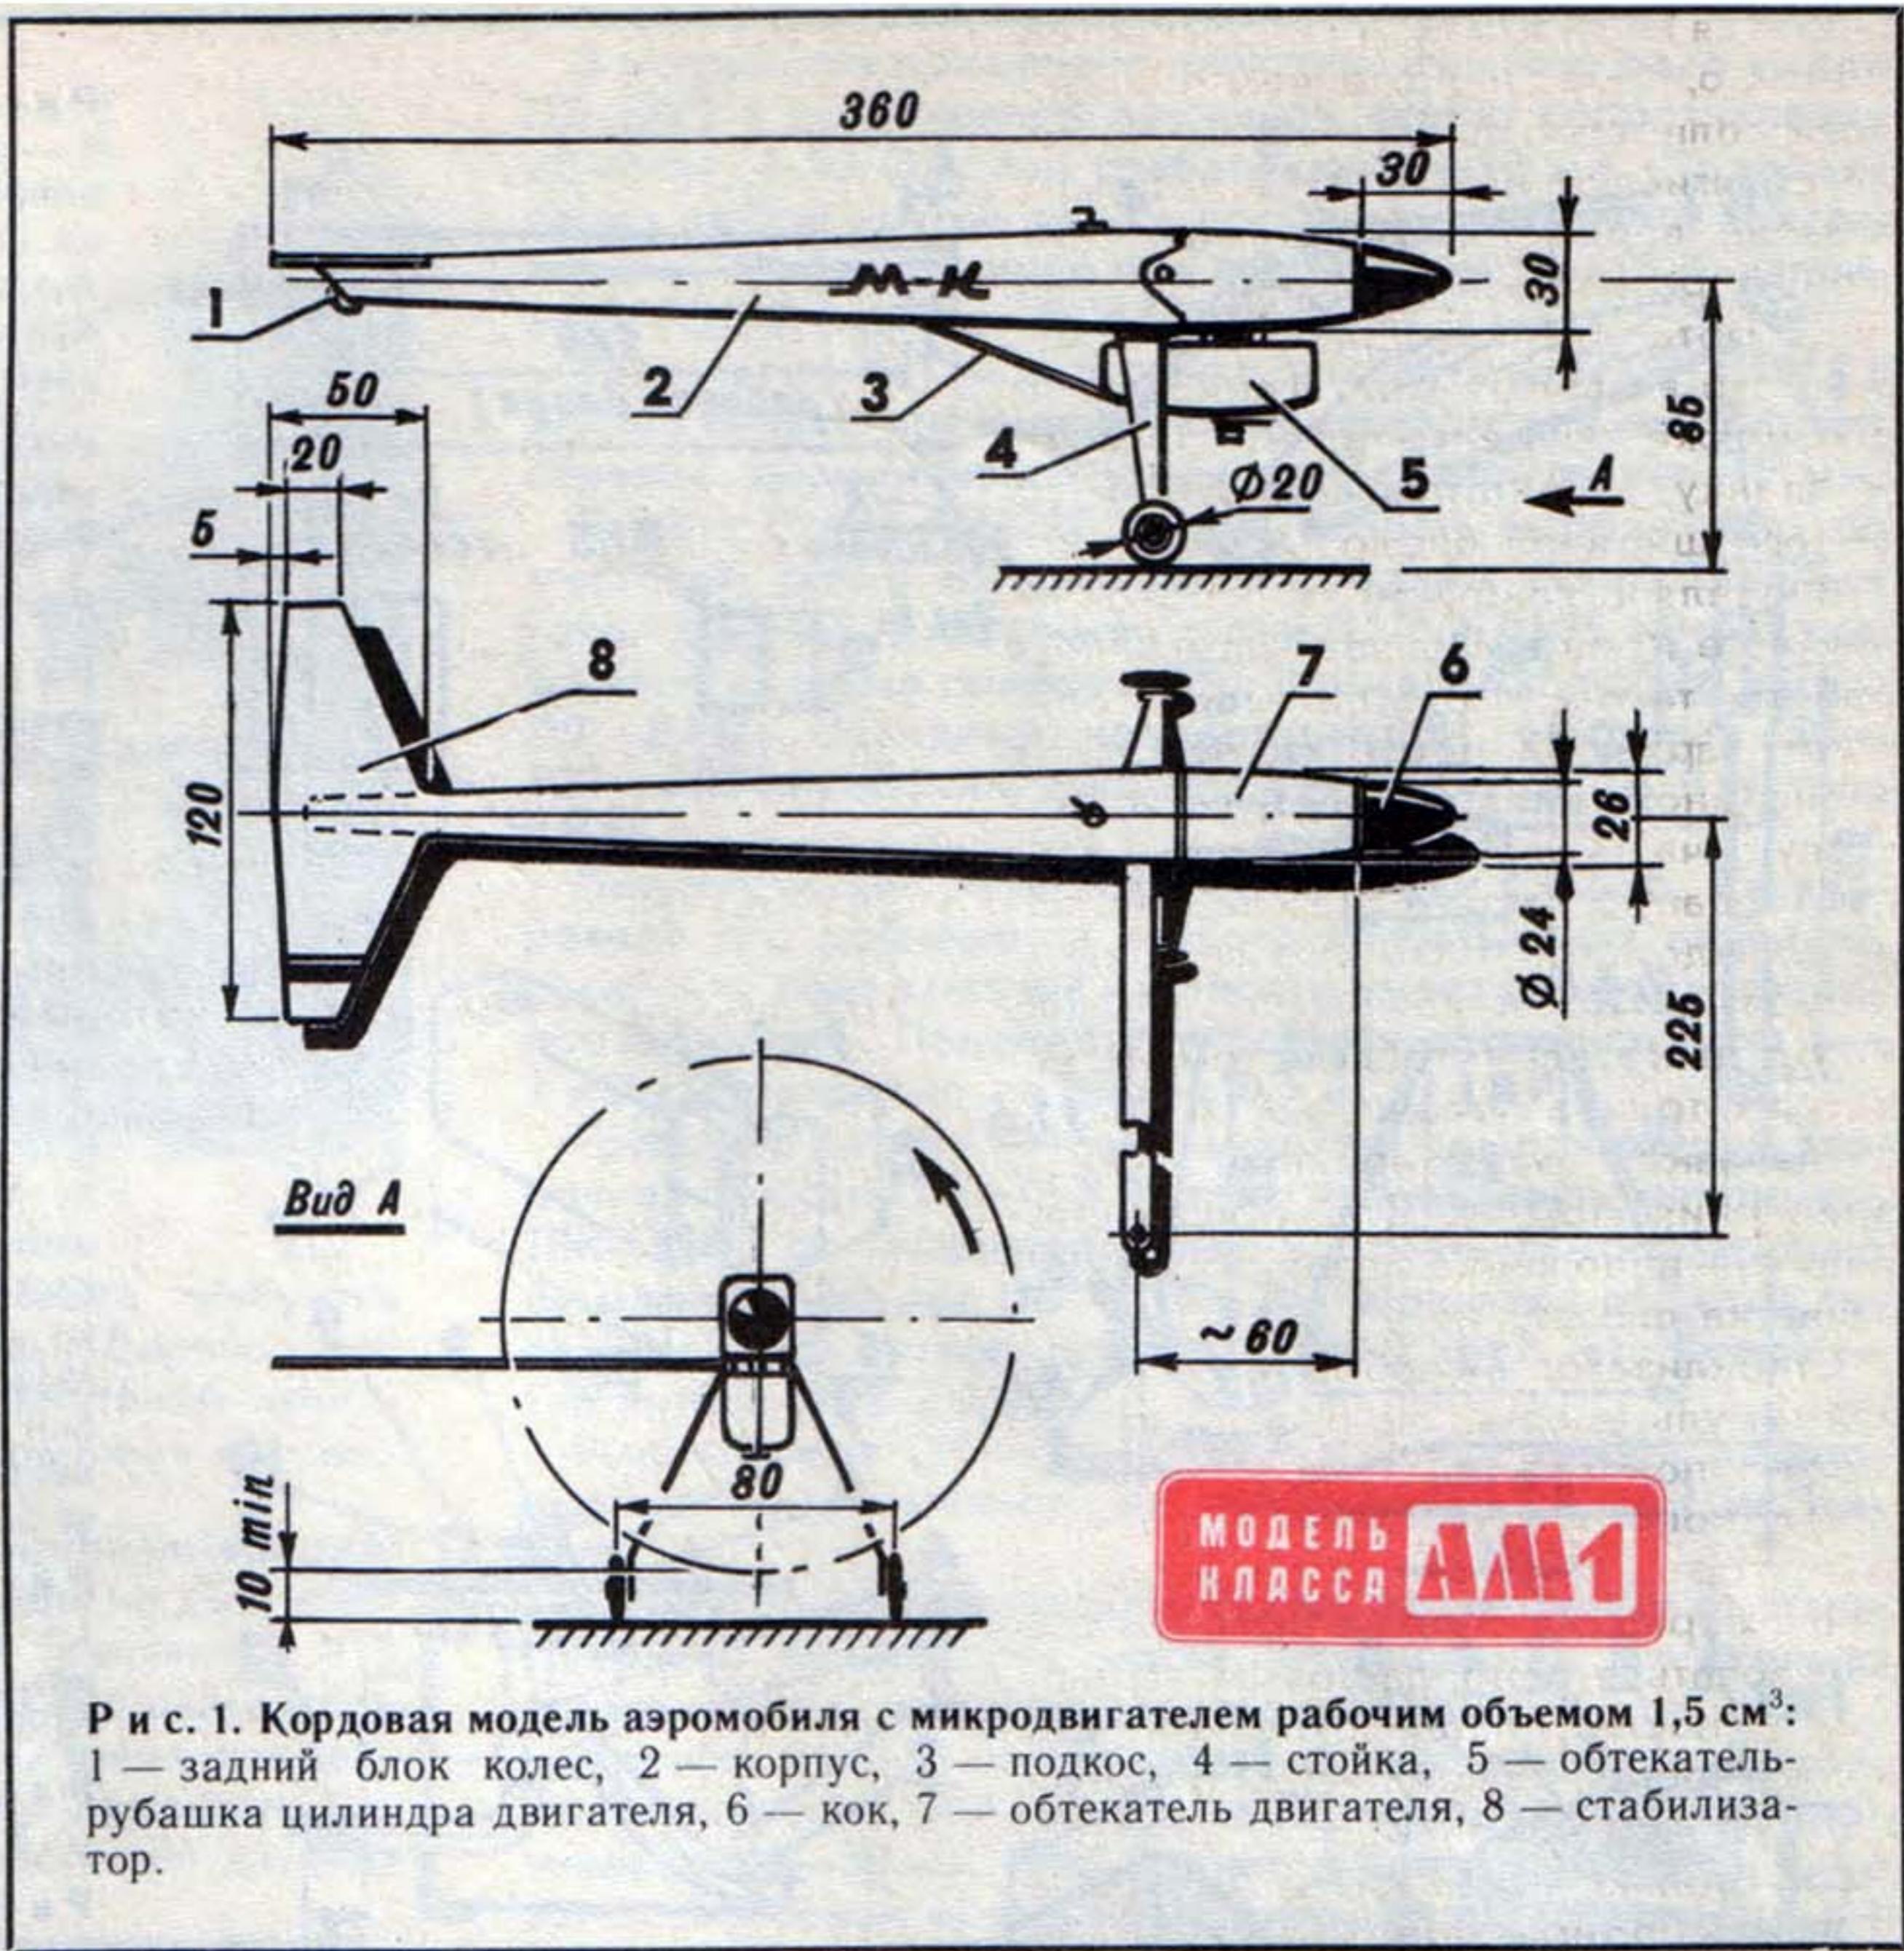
Кордовая модель аэромобиля с микродвигателем рабочим объемом 1,5 см<sup>3</sup>: 1 — задний блок колес, 2 — корпус, 3 — подкос, 4 — стойка, 5 — обтекатель-рубашка цилиндра двигателя, 6 — кок, 7 — обтекатель двигателя, 8 — стабилизатор.
